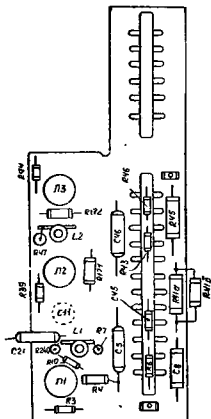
Схема расположения основных деталей на усилителе сигналов запуска
